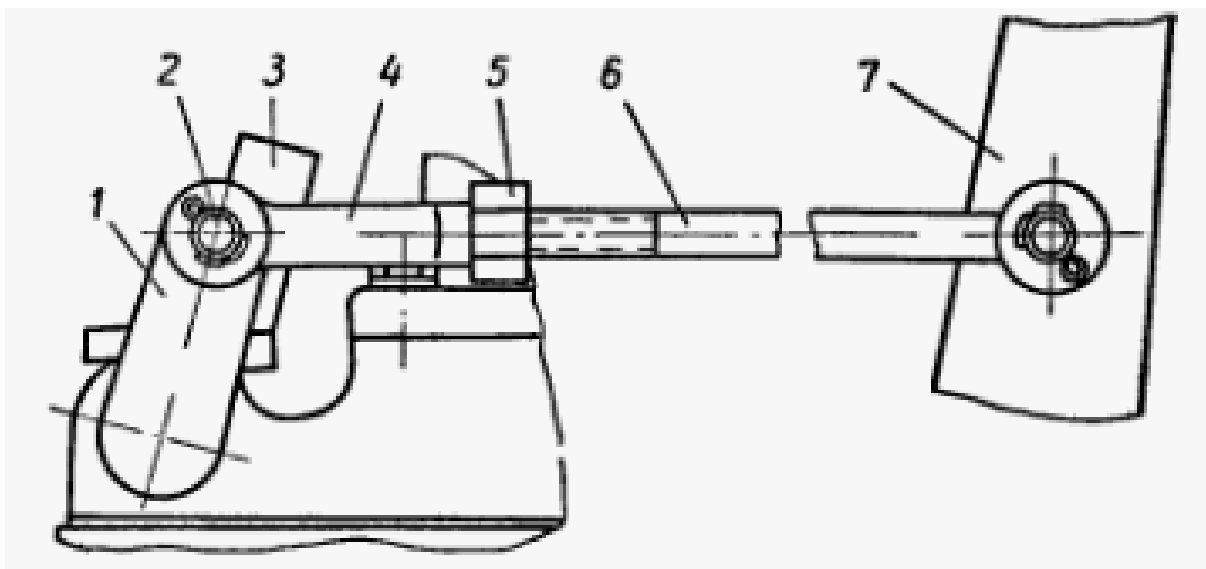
Регулювання механізму блокування перемикання діапазонів КПП ХТЗ 1 – важіль; 2 – палець; 3 – покажчик; 4 – вилка; 5 – контргайка; 6 – тяга; 7 – педаль муфти зчеплення.
